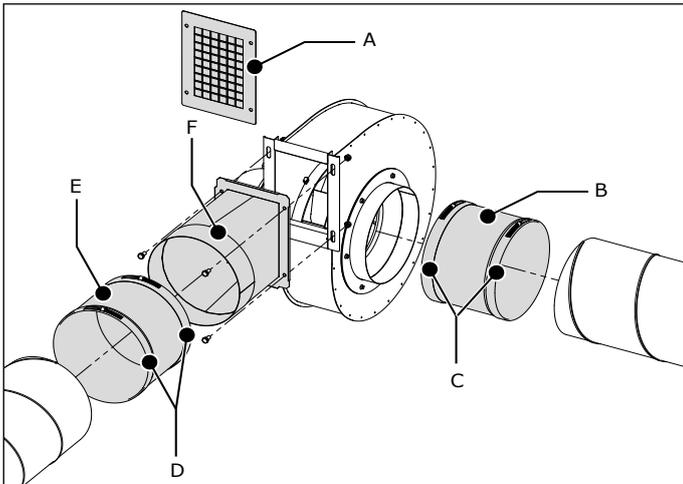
Connexion de conduit du FUA-3000/4700
